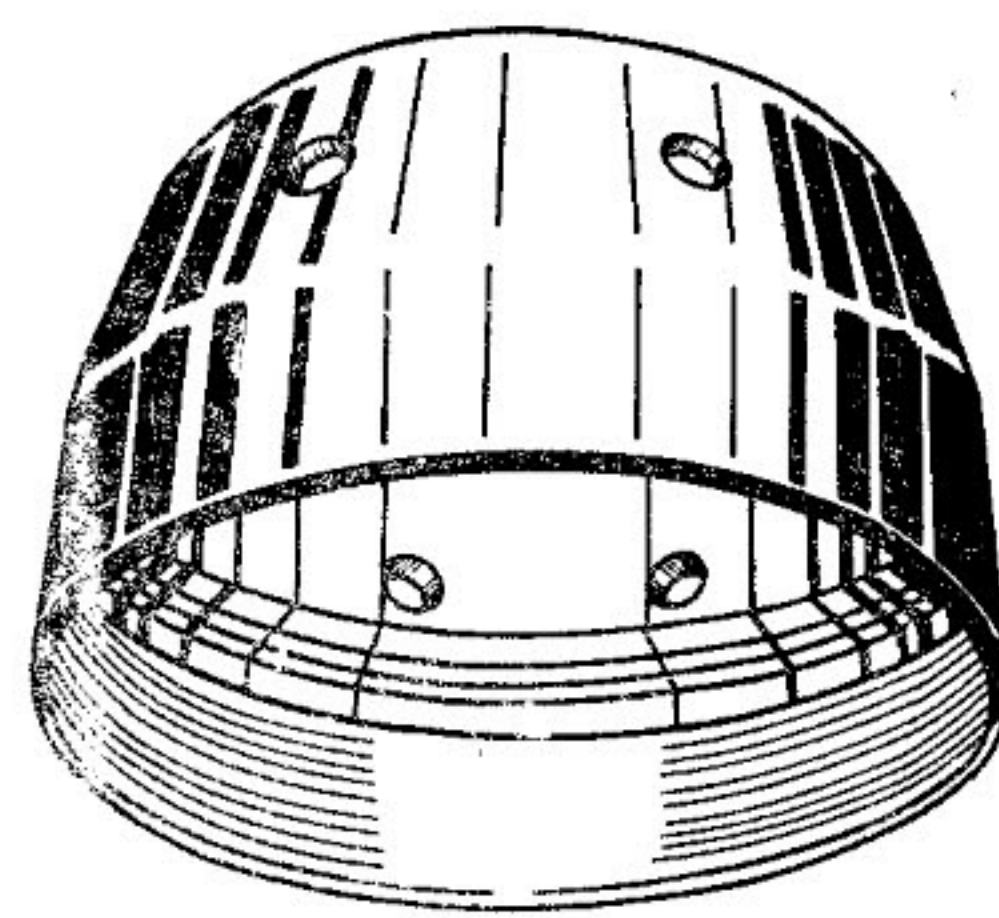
Приспособление для защиты резьбы вала несущего винта при монтаже втулки и автомата перекоса
